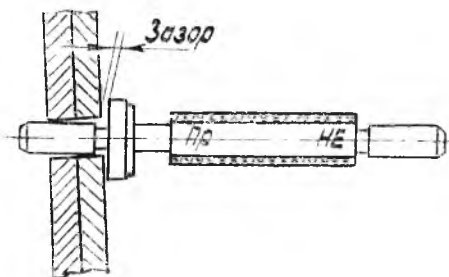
Установка калибр-пробки для контроля положения оси отверстия относительно поверхности детали
